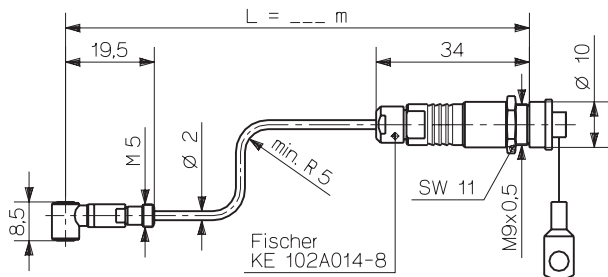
Kraftsensor Typ 9213Bsp mit Kabel und Stecker (Standardlängen: 0,2/0,4/0,6/0,8/1,2 m)
